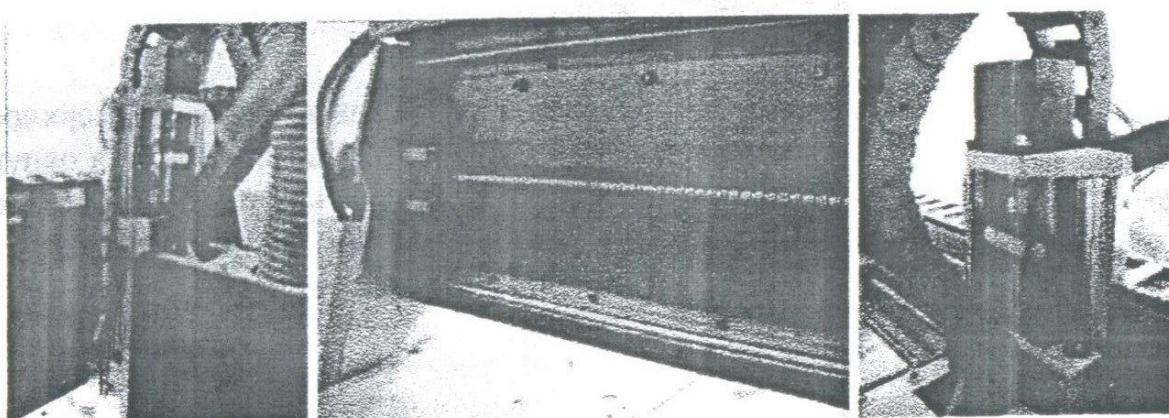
Общий вид 3-х координатного фрезерного станка с ЧПУ
